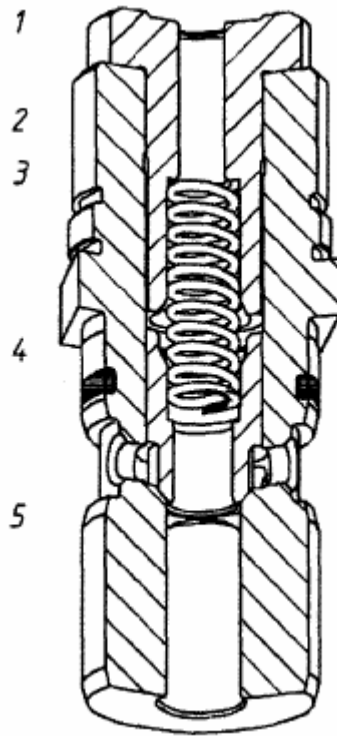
Всмоктуючий клапан ТНВД дизеля серії МС фірми MAN : 1 - напрямна пружини; 2 - корпус клапана; 3 - пружина; 4 - клапан; 5 - напрямна втулки плунжера.
